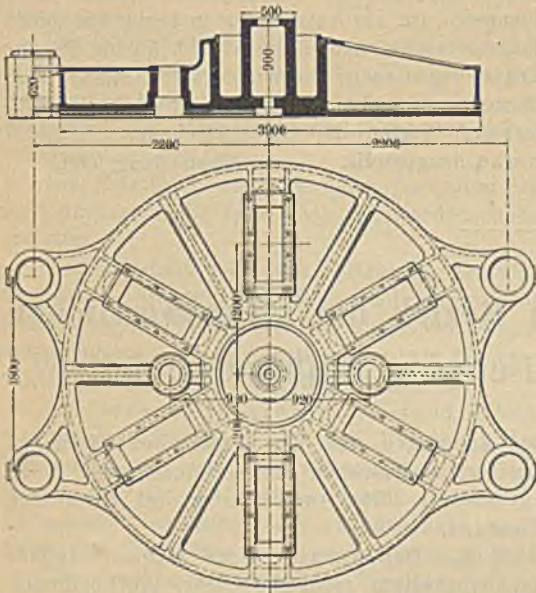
Führungsstück zu einer hydraulischen Kumpelpresse von 750 t Druck. Gewicht 28 000 kg. (Gutehoffnungshütte.)
